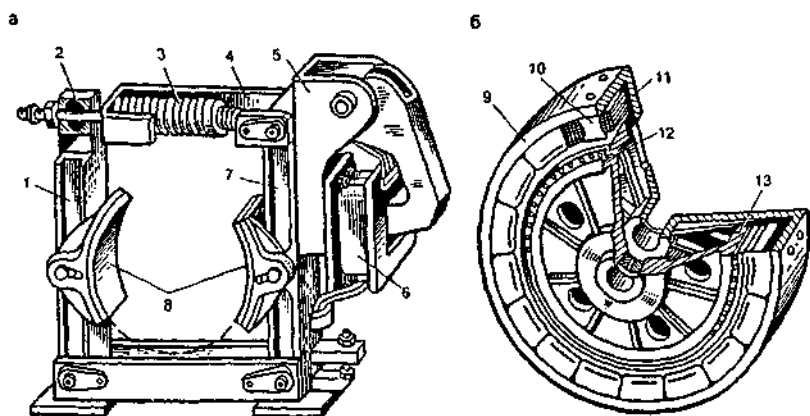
Электромагнитные устройства кранов и механизмов: а - тормозной электромагнит; б - электромагнитная муфта; 1, 7 - рычаги; 2 - шпилька; 3 - пружина; 4 - скоба; 5 - электромагнит; 6 - катушка; 8 - тормозные колодки; 9 - внешний (статорный) обод муфты; 10 - полюс; 11 - обмотка полюса; 12 - «беличья клетка»; 13 - внутренний (роторный) обод муфты
